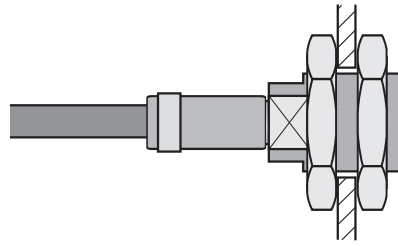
Geschirmter Sensor mit Gewinde in Standardmontage
